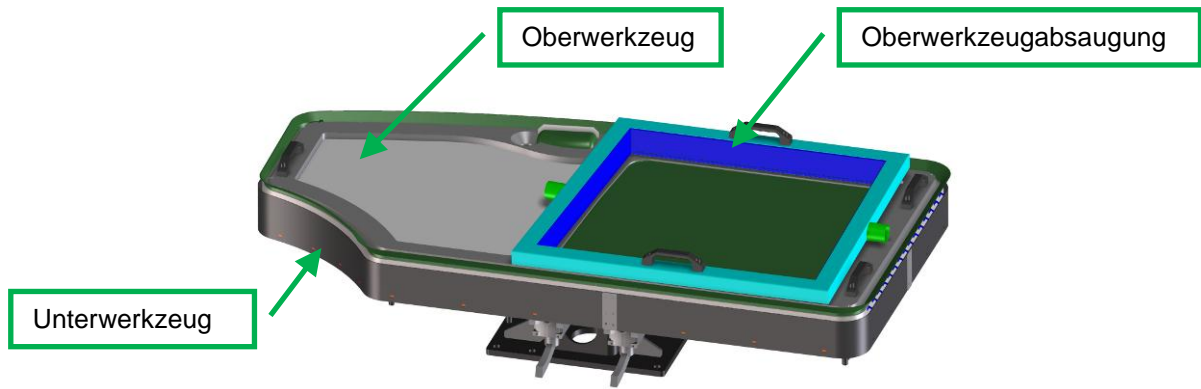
Spannvorrichtung für CFK-Wohnmobiltür Oberwerkzeug
